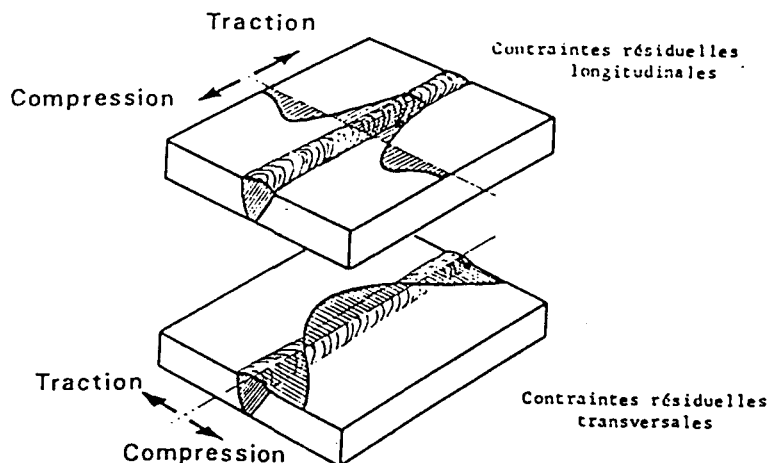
Profil de contraintes résiduelles en surface d'un assemblage soudé bout-à-bout [LIEU88]
